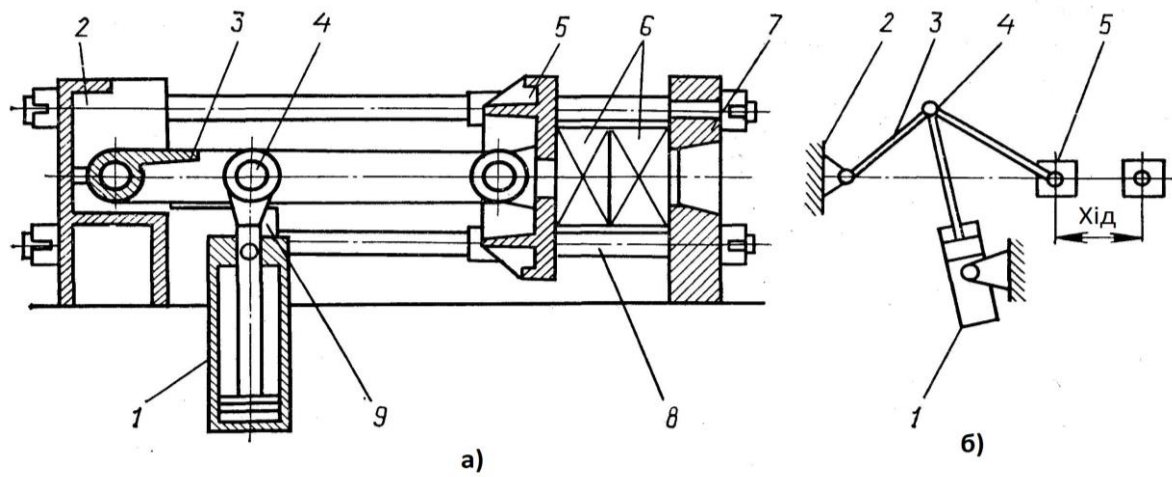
Конструктивна (а) і кінематична (б) схеми шестиланкового механізму замикання форми з гідроциліндром, що коливається:
